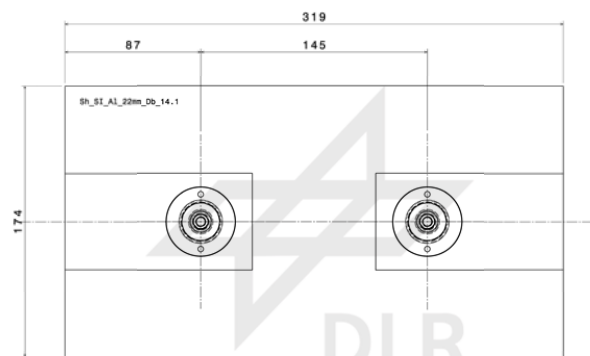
Dimensionsmaße Shear-Testpanel, 618 HC, 22 mm, beidseitig verstärktes Schraubinsertkonzept.
